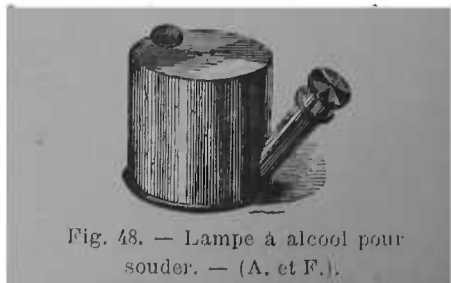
Lampe à alcool pour souder. — (A. et F.).
